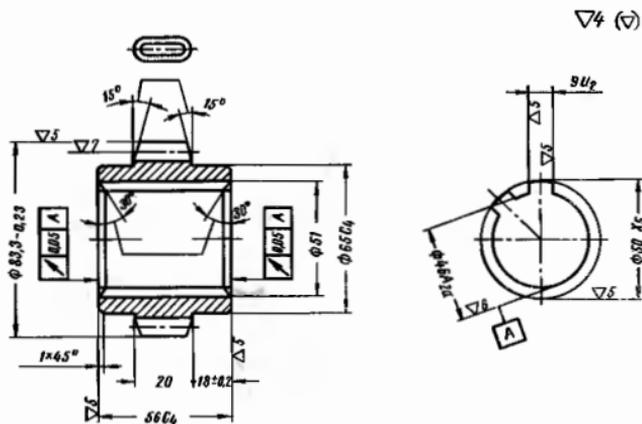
Зубчатое колесо. Деталь 6МЭ9.3-48Н
